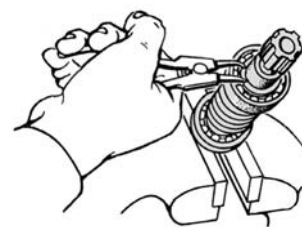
Снятие стопорного кольца крепления подшипника червяка.
